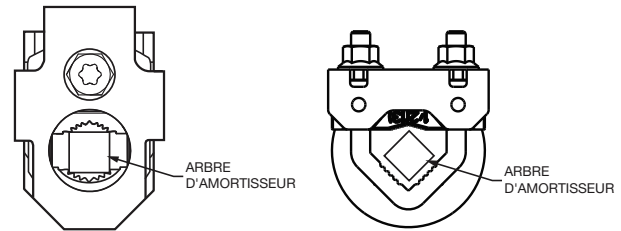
Montage approprié pour arbre d'amortisseur carré.
